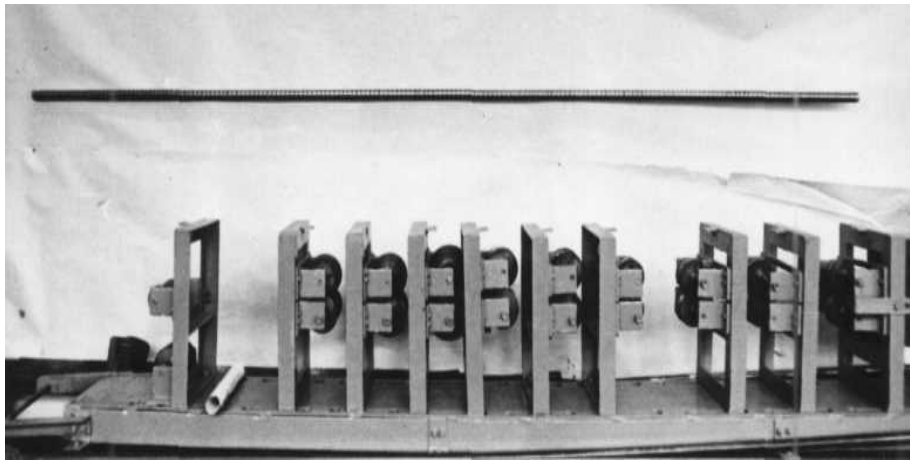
Пристрій для формоутворення трубчастої заготовки зі стрічки
